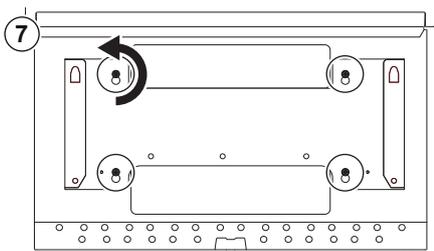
Sollevare la piastra di montaggio della scheda elettronica
